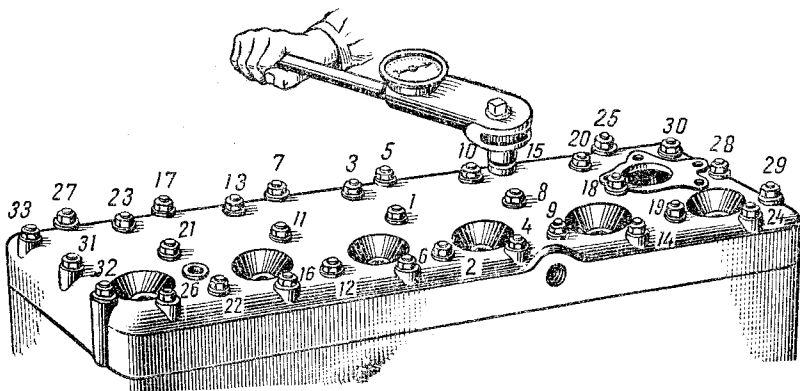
Последовательность затяжки гаек крепления головки цилиндров двигателя ГАЗ-52-01.
